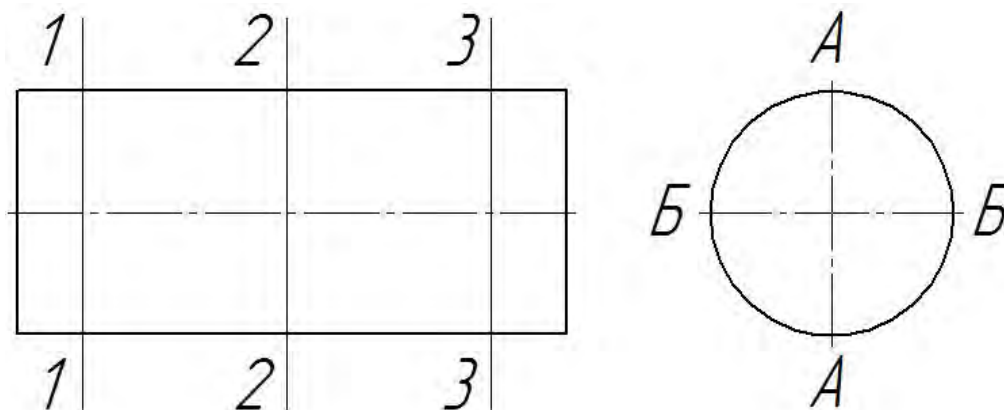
Схема контроля размеров гладкой наружной цилиндрической поверхности
